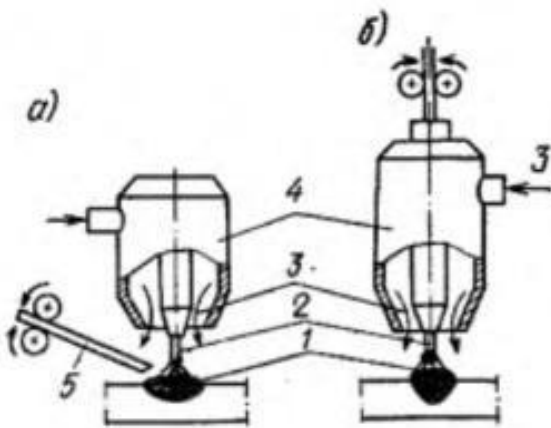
Схеми зварювання в захисних газах а, б - неплавким, плавким електродом; 1 - зварювальна дуга; 2 - електрод; 3 - захисний газ; 4 - газове сопло (пальник); 5 - присадний дріт.
